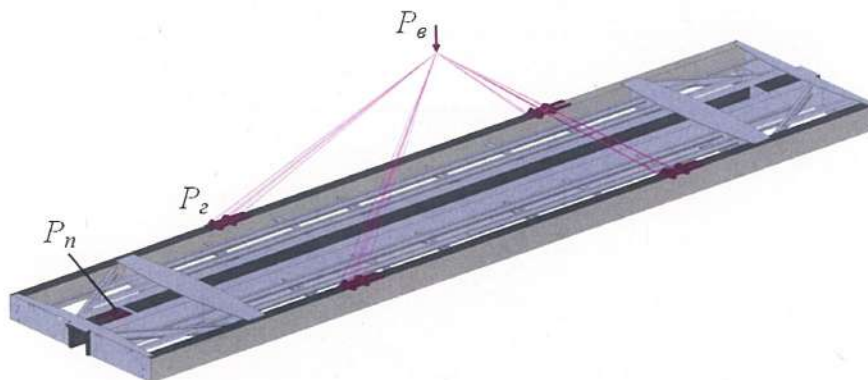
Розрахункова схема несучої конструкції вагона-платформи
